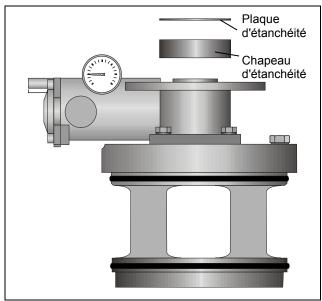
Dépose de la plaque d'étanchéité et du chapeau d'étanchéité
